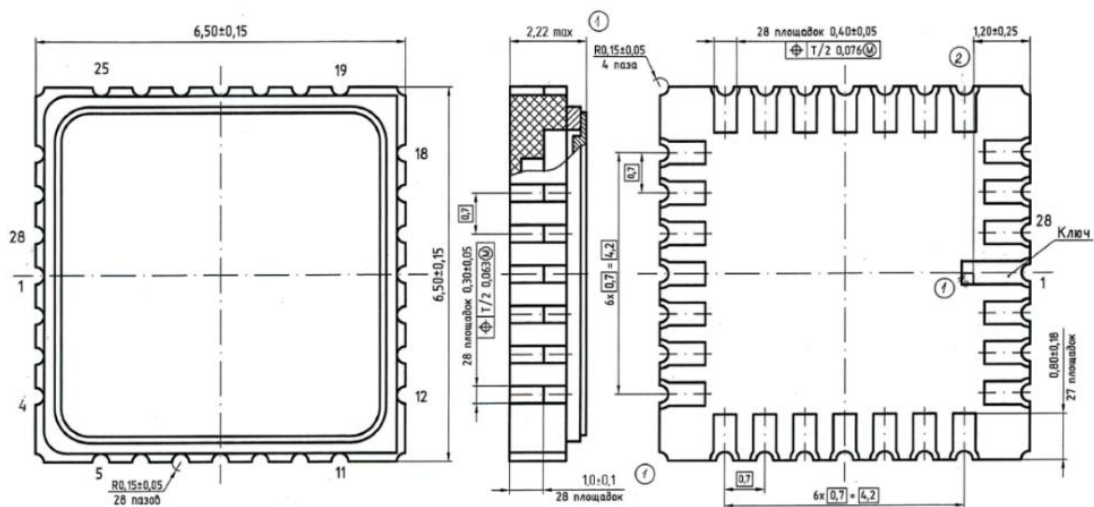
Габаритный чертёж корпуса МК 5123.28-1.01 (размеры в мм)
